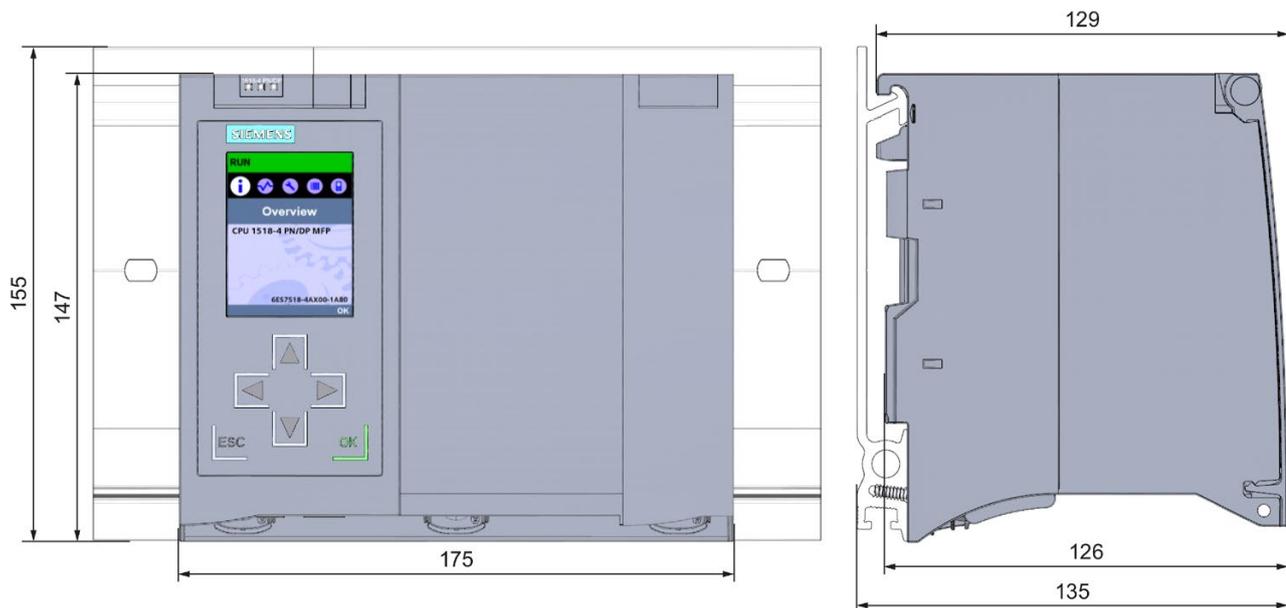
Maßbild der CPU 1518-4 PN/DP MFP, Front- und Seitenansicht
